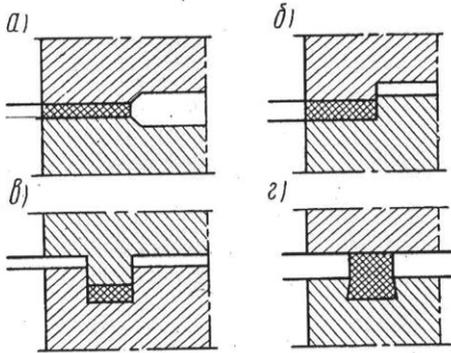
Типы уплотнительных поверхностей фланцев:
